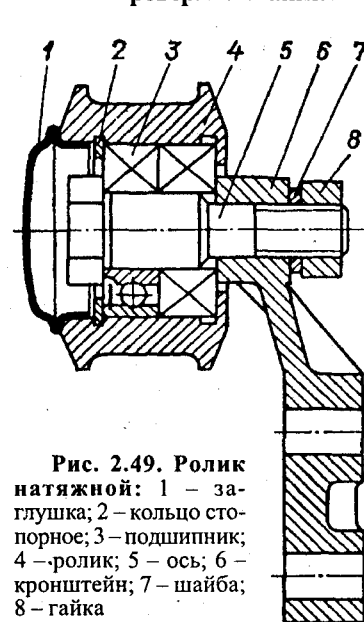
Ролик натяжной: 1 – заглушка; 2 – кольцо стопорное; 3 – подшипник; 4 – ролик; 5 – ось; 6 – кронштейн; 7 – шайба; 8 – гайка
